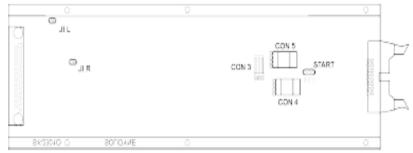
Módulo de línea 2801 (Vista lado soldaduras)
